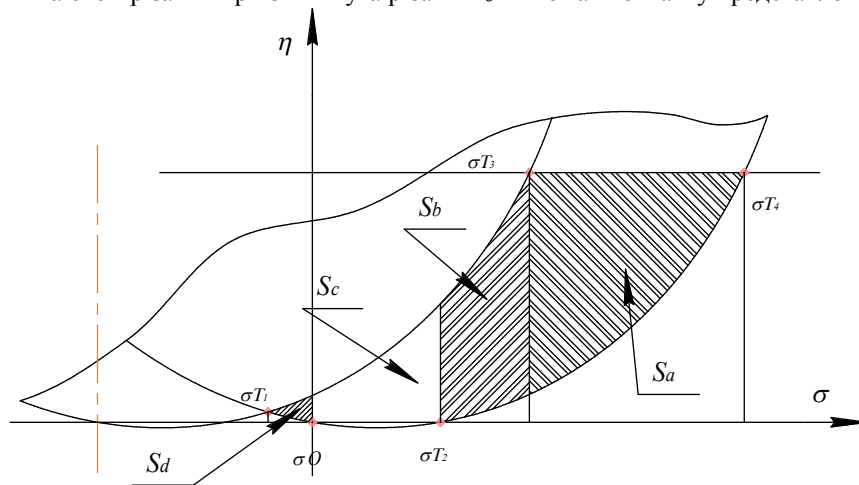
Схема визначення площі контакту передньої поверхні пластини з матеріалом заготовки
